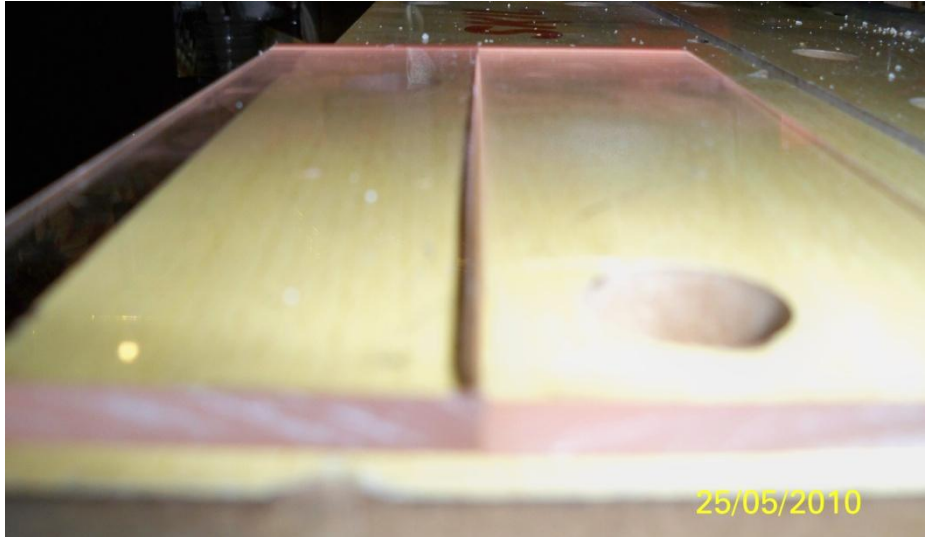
Placas de acrilico que seran soldadas
